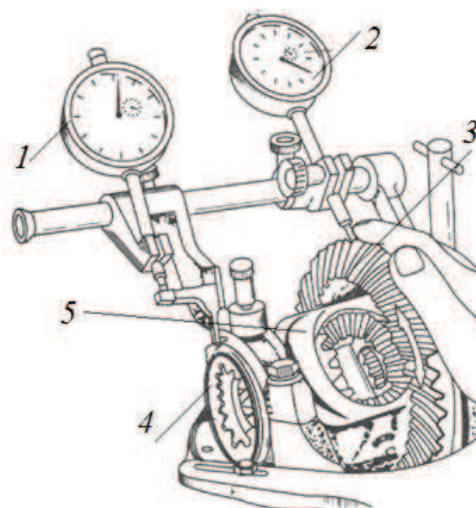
Схема регулирования бокового зазора в зацеплении главной передачи с помощью специального контрольного приспособления: *1, 2* – индикаторы часового типа; *3* – ведомое колесо; *4* – регулировочная гайка; *5* – корпус дифференциала
